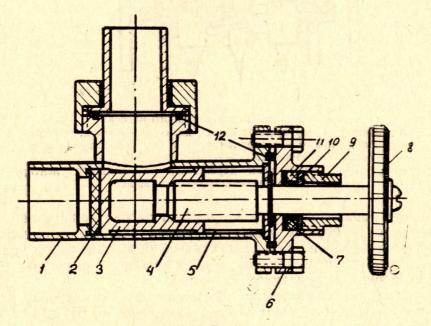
Вентиль: 1 — корпус вентиля, 2 — фторопластовый диск, 3 — клапан, 4 — винт, 5 — стопорная втулка, 6 — фланец, 7 — фторопластовая втулка, 8 — маховичок, 9 — гайка, 10 — шайба, 11 — резиновая прокладка
